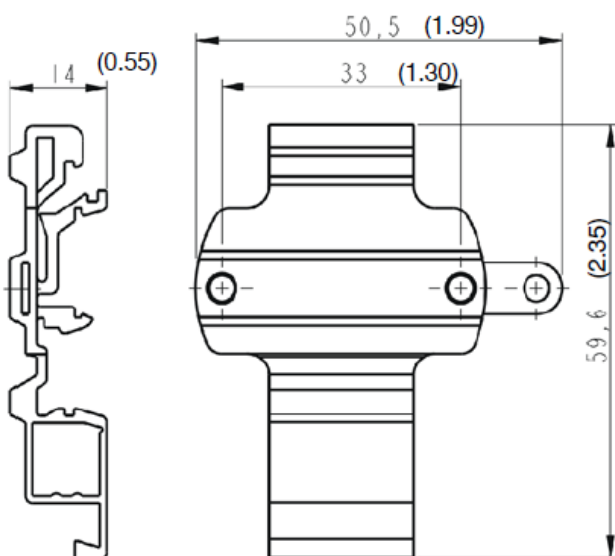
Габаритные размеры DIN – рейки (7NG3092--8KA)
